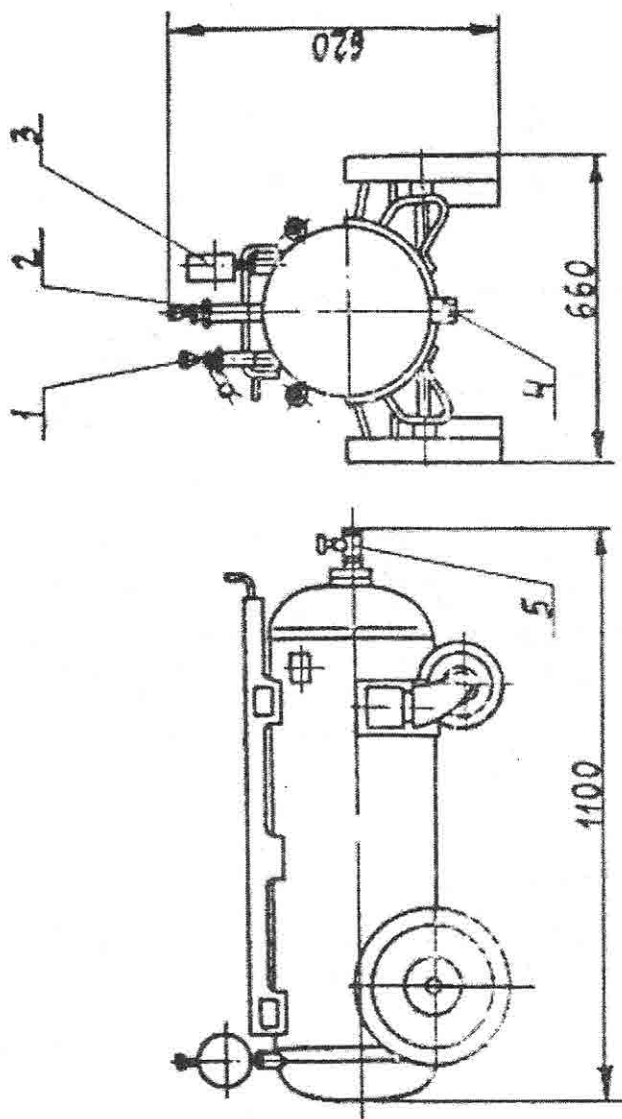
Ресивер установки компрессорной, модель К-5 или модель К-6:
